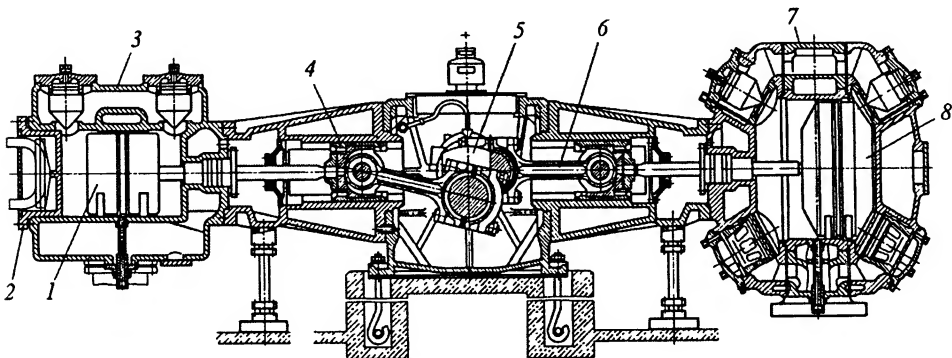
Двухрядный оппозитный воздушный компрессор 2М10-50/8
